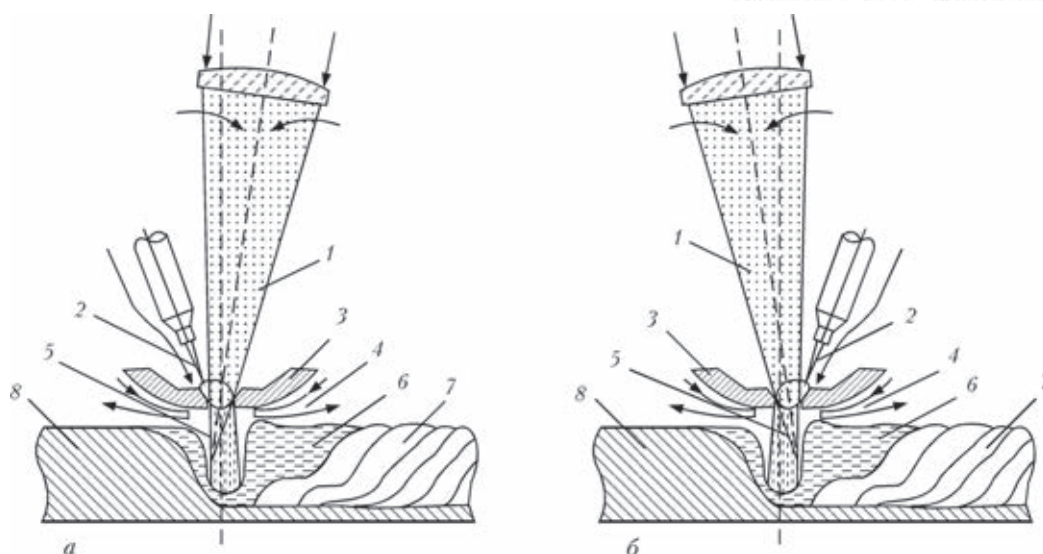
Схемы процесса гибридной лазерно-плазменной сварки с расположением плазменной горелки перед (а) и за (б) лазерным пучком [15]: 1 — сфокусированное лазерное излучение; 2 — неплавящийся электрод; 3 — плазмообразующее сопло; 4 — защитный газ; 5 — плазменный разряд; 6 — сварочная ванна; 7 — металл шва; 8 — основной металл
